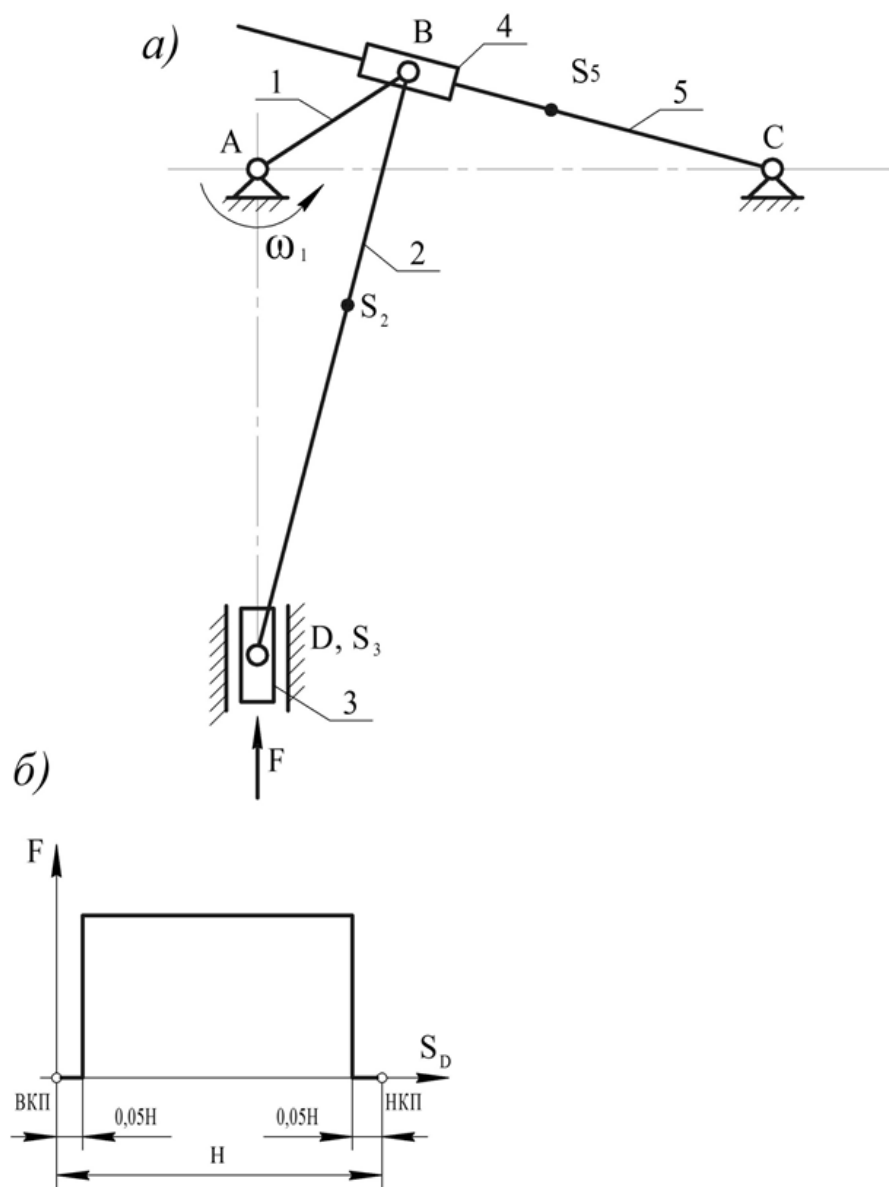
Схема рычажного механизма зубодолбежного станка для нарезания цилиндрических колес
